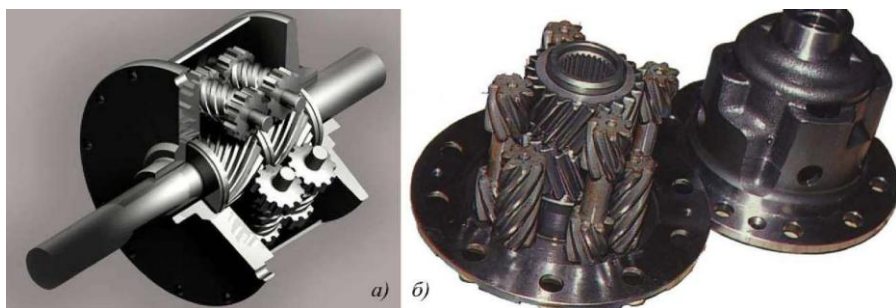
Диференціали «Готтзеп»: а - черв'ячний; б – циліндричний.
